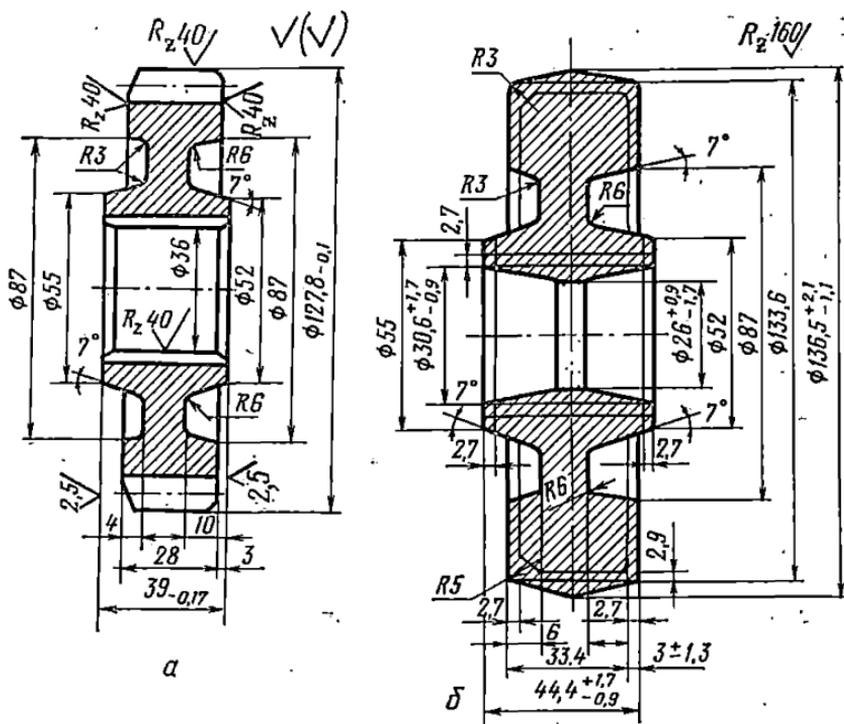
Цилиндрическое зубчатое колесо трактора:
